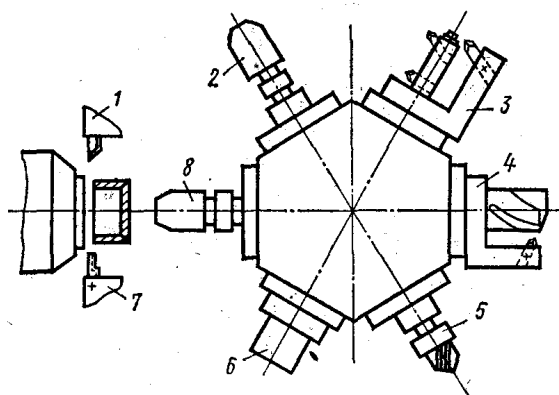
Схема обработки втулки на токарно-револьверном станке
